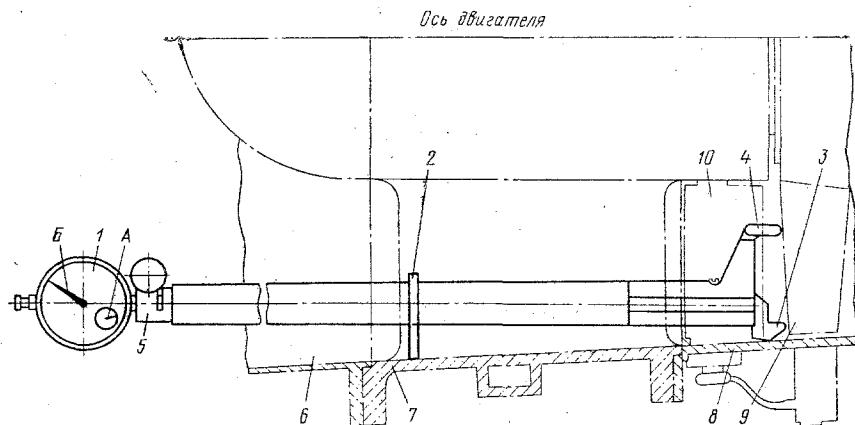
Схема замера износа передней кромки лопаток первой ступени ротора компрессора:
